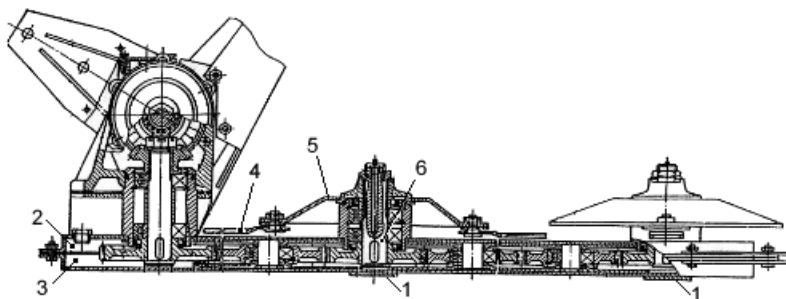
Конструкция многороторного рабочего органа косилки с боковым приводом.
